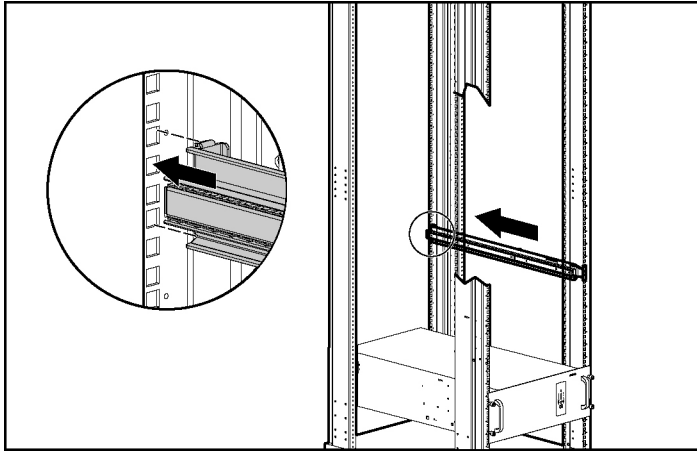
Einstecken der gefederten Schienen in die Rack-Rückseite
